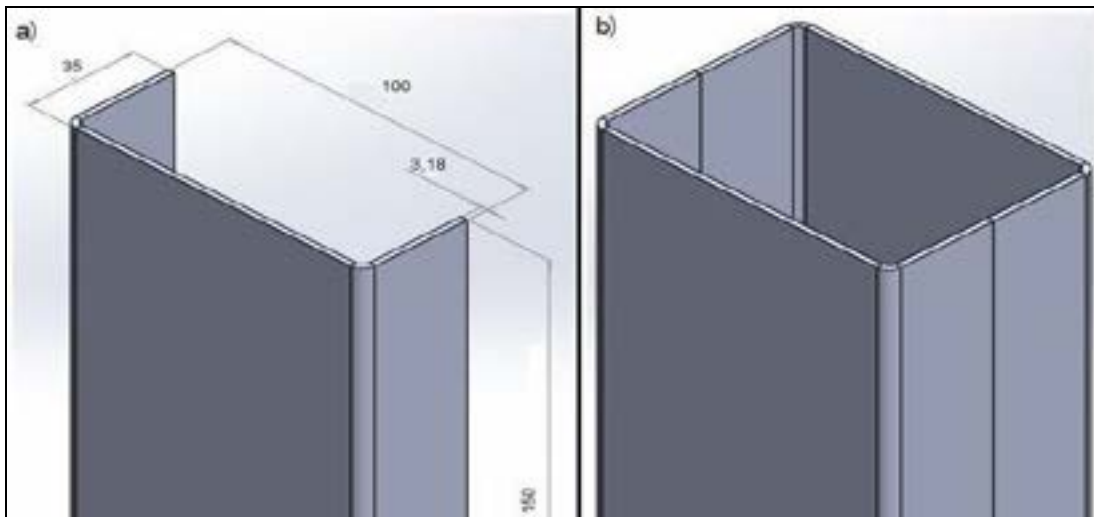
(a) Dimensões do corpo de prova; (b) Posicionamento dos corpos para soldagem.
